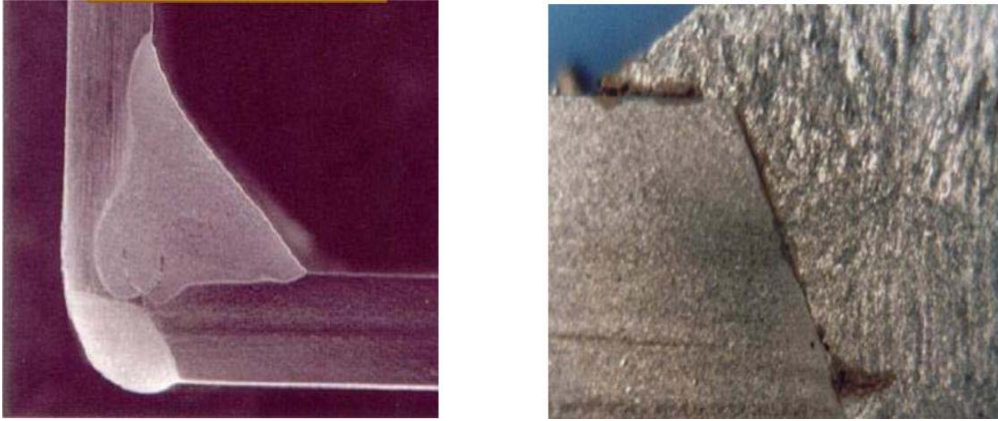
Manque de fusion de la soudure<sup>(6)</sup>.
